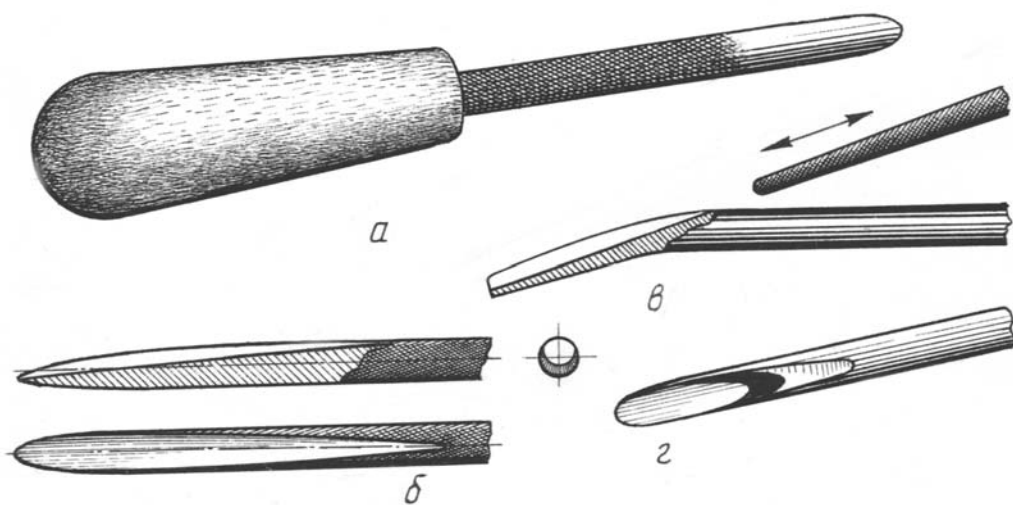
Резец: а – изготовленный из круглого напильника (вид на стель с обратной стороны канавки); б – чертёж стелья полукруглого резца; в – вытачивание канавки на изогнутом (отожжённом) стержне; г – резец, изготовленный из круглого стержня сверлением канала с торца
